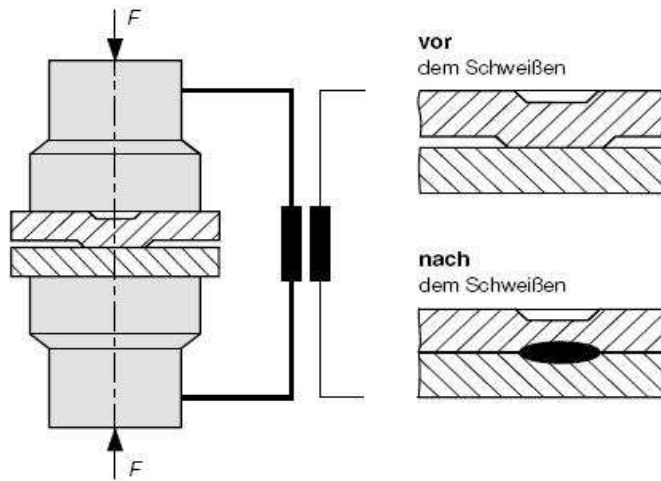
Punktentstehung beim Buckelschweißen mit geprägten Buckeln<sup>[ST03]</sup>
